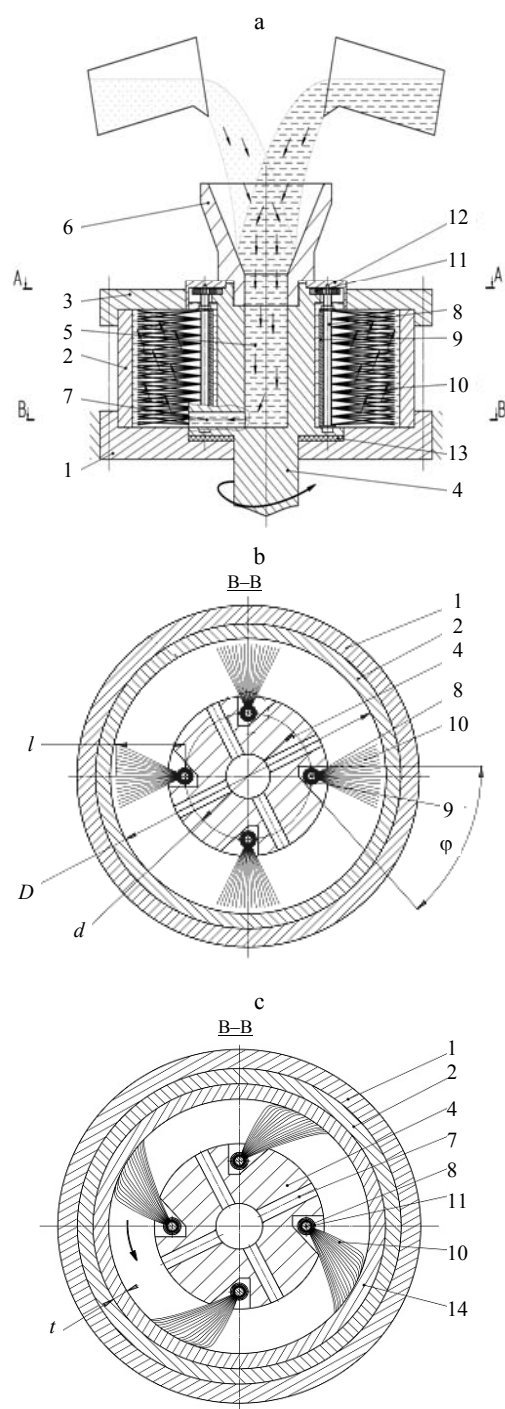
Устройство для заливки подшипника скольжения: а – общая схема; б – сечение В–В с пазом в виде треугольника; с – сечение В–В для случая с закристаллизовавшимся подшипником скольжения (отливкой)
